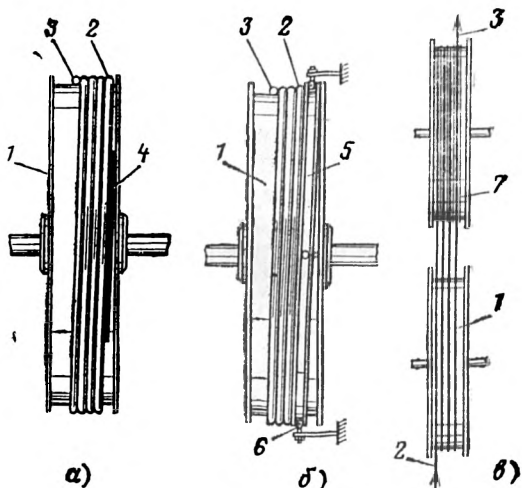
Тяговые колеса с приспособлениями для сдвига витков кабеля.
